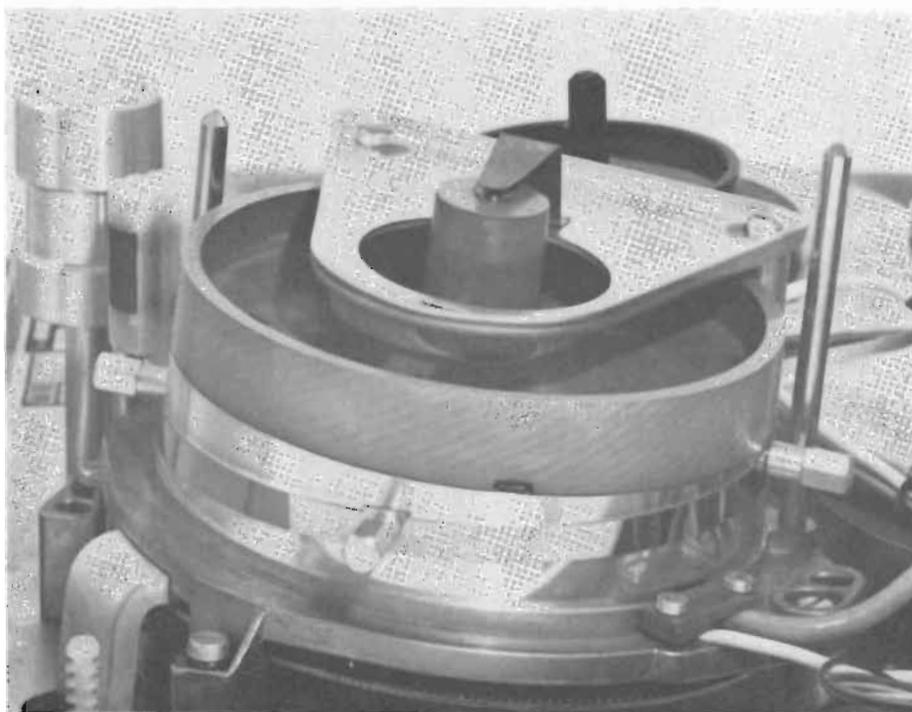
Tamburo porta testina disposto obliquamente (LDL 1000).
